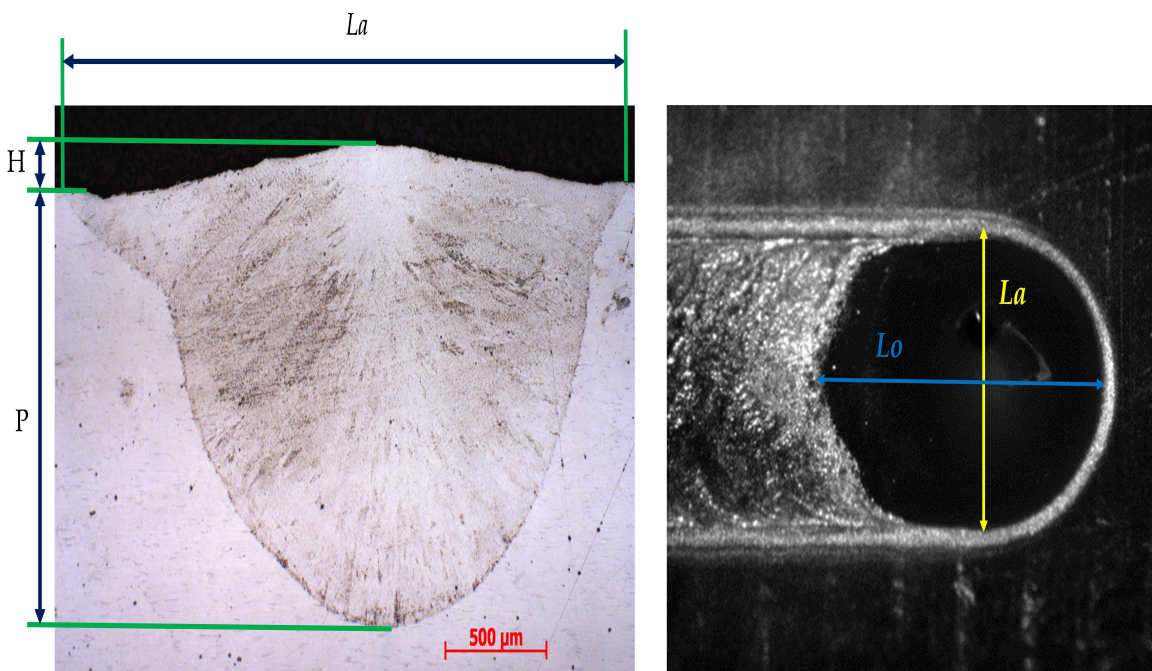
Morphologie du bain de soudage (316L).
